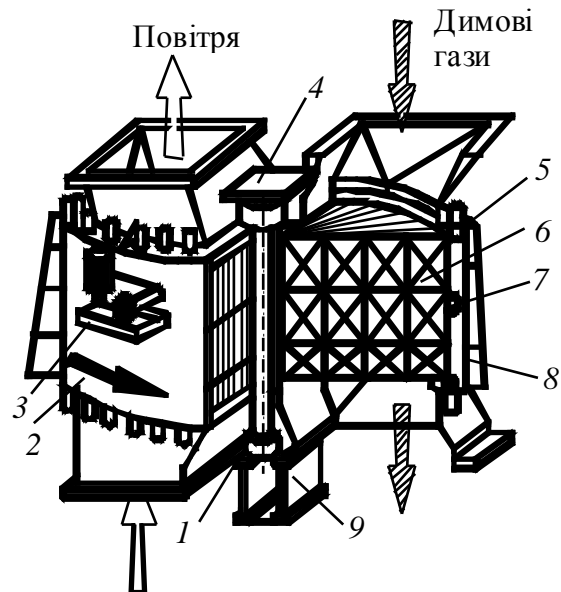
Схема регенеративного повітропідігрівника: 1 – вал; 2 – обертовий корпус; 3 – поворотний механізм; 4 і 9 – верхня і нижня опори; 5 і 8 – зовнішній і внутрішній кожух; 6 – поверхня теплообміну; 7 – ущільнення
